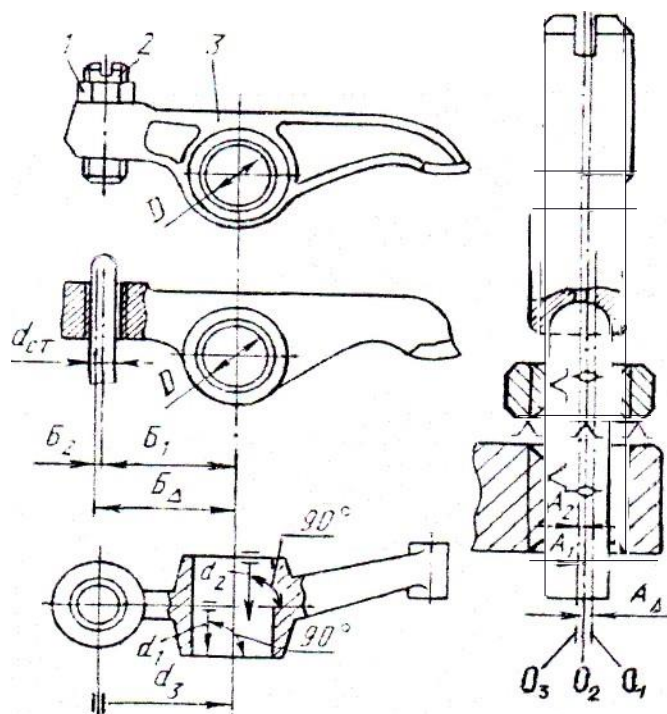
Схема базування деталей коромисла клапана: 1- контргайка;
